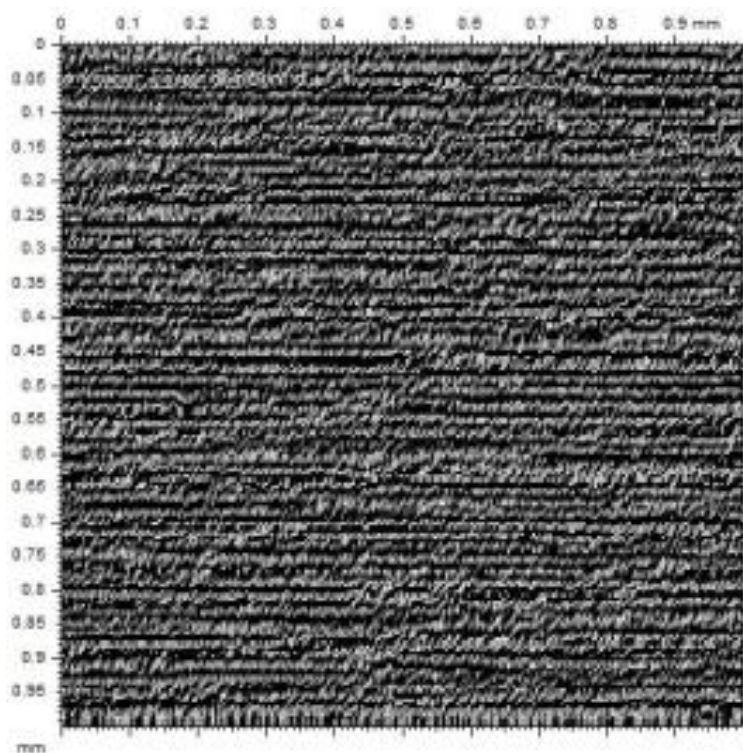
2D zobrazení broušeného povrchu pryže NBR+BR
